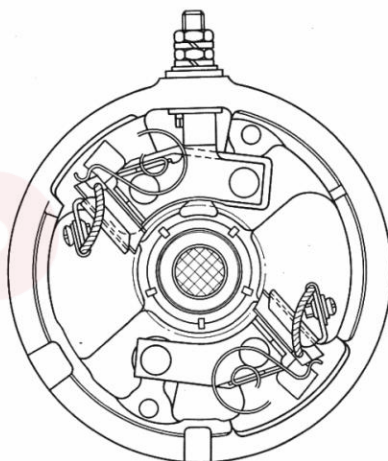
Querschnitt der Lichtmaschine durch die Ankerwelle mit Ansicht auf das Kollektorlager.
